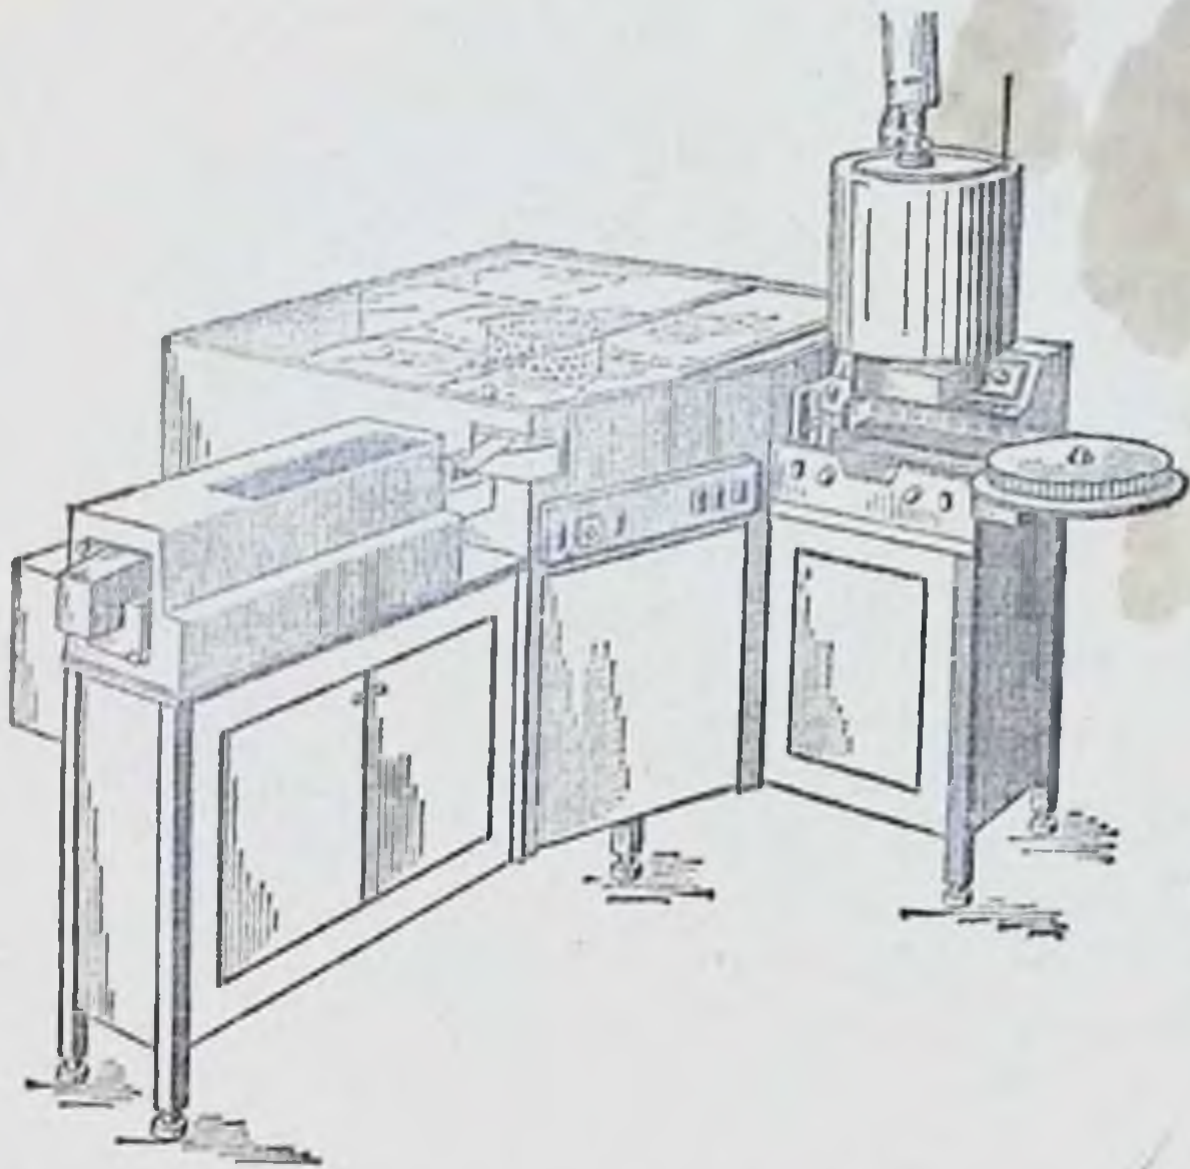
Автомат для изготовления и упаковки суппозиториев.
